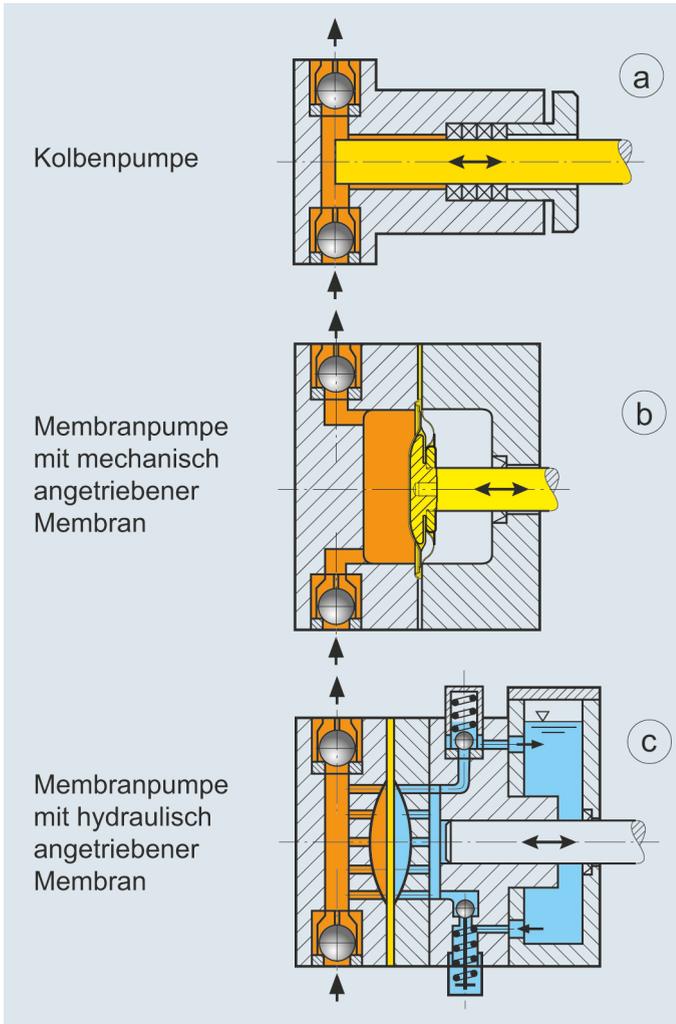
Pumpenkopf-Bauarten (Prinzipien)
